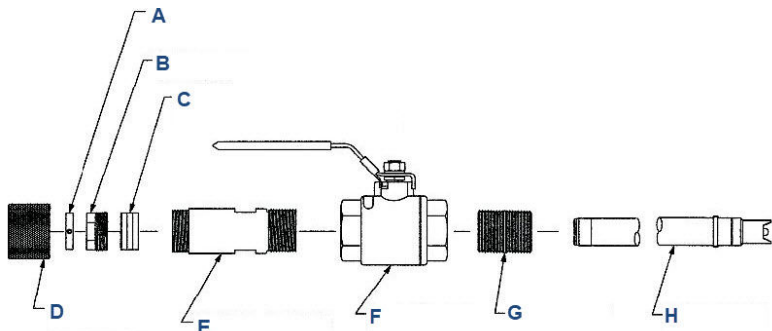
Комплект для сборки шарового клапана (PN 23765-00) и датчика
